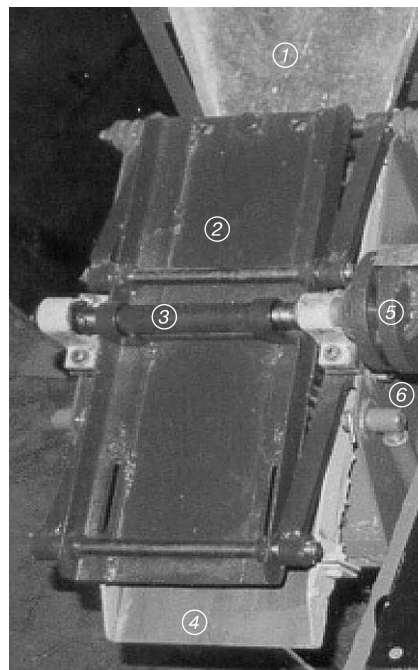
Устройство для дробления: 1 – подающий лоток, 2 – подвижная плита, 3 – вал подвижной плиты, 4 – лоток камеры дробления, 5 – соединительная муфта, 6 – корпус
